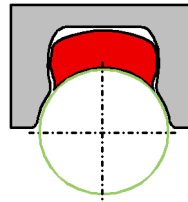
Schaltfinger und Schaltmaul für Handschaltgetriebe
